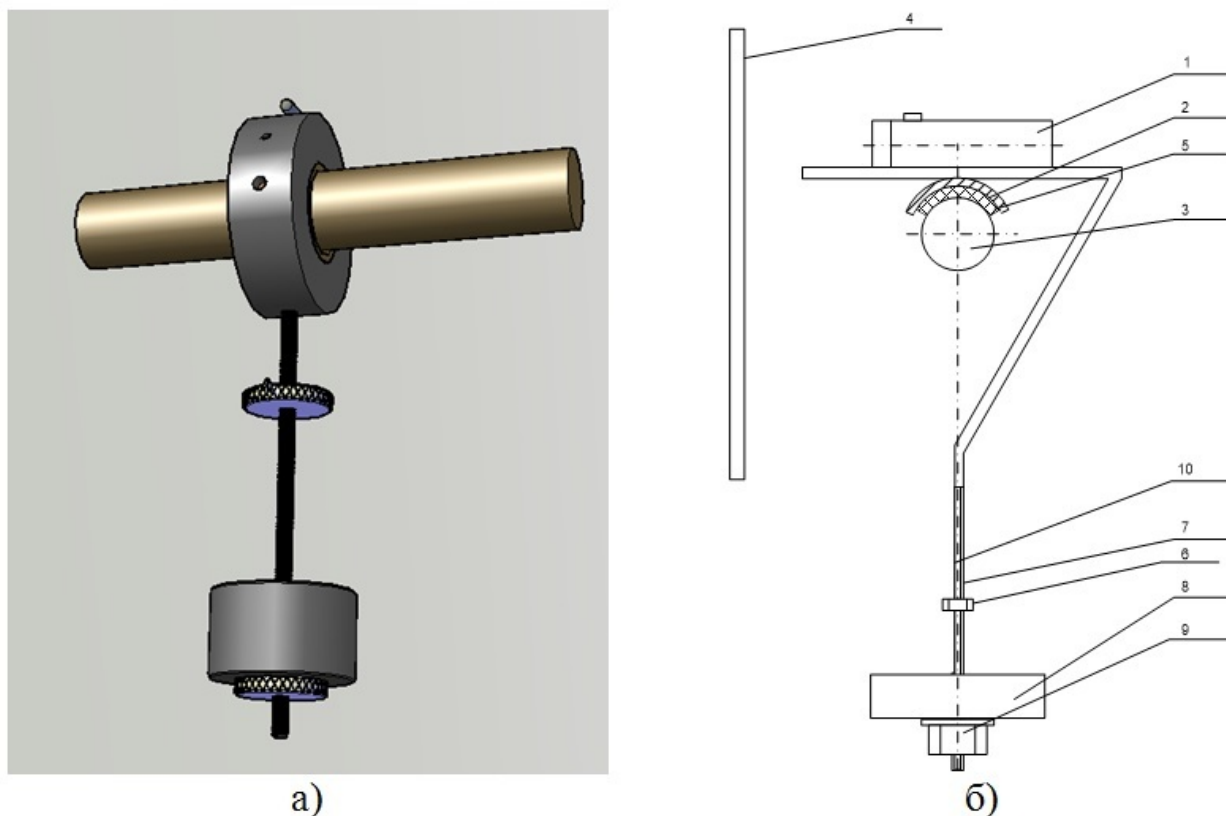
Эскиз маятника: а — внешний вид маятника; б — чертёж трибомаятника.
